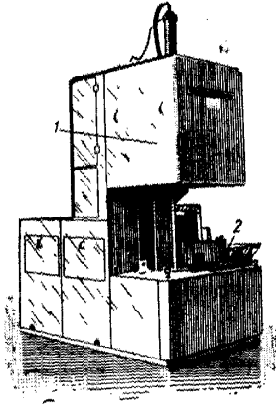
Нагреватель с вертикальным индуктором фирмы «Левин»:
